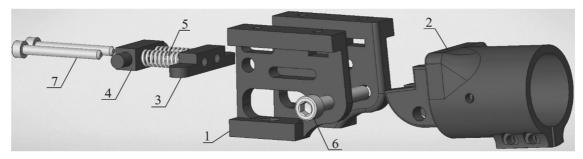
Конструкция механизма складывания: 1 — боковая пластина; 2 — держатель луча; 3 — бегунок; 4 — направляющая; 5 — пружина; 6 — ось
